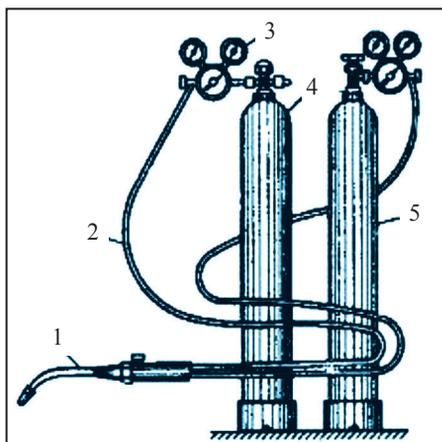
Оборудование для газосварки: 1 – горелка; 2 – шланги; 3 – редуктор; 4 – кислородный баллон; 5 – ацетиленовый баллон.
